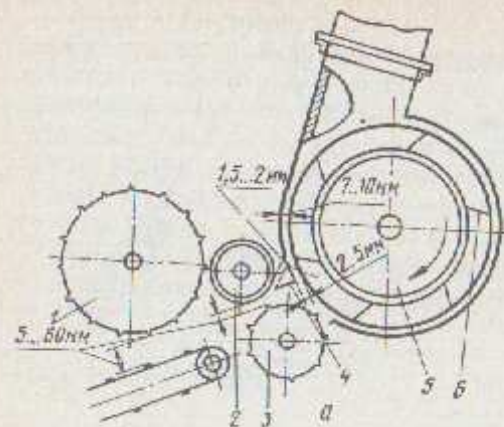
Питающий и измельчающий аппарат, прицепного силосоуборочного комбайна:
